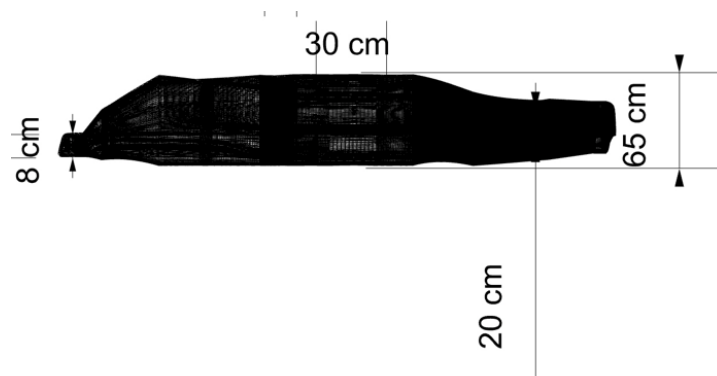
Planos Técnicos del tablero de un autobús. Vista frontal.
